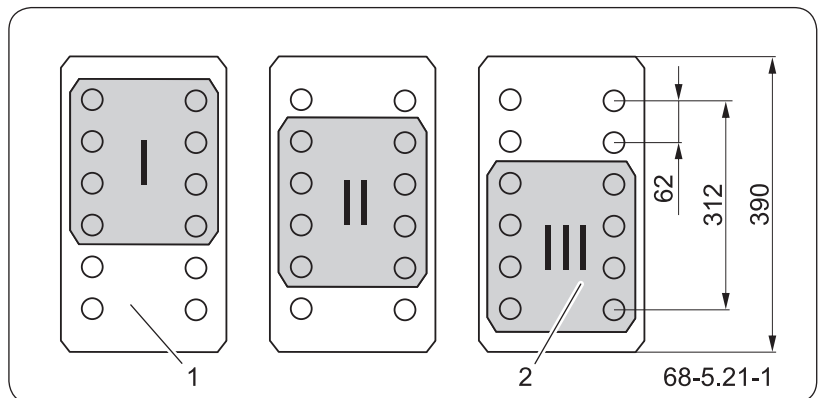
Ausrichtung der Deichsel zur Stirnplatte des Rahmens.
